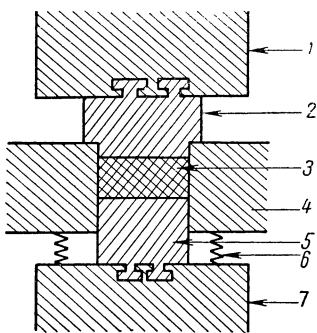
Принципиальная схема прессформы для одновременного двухстороннего прессования.
